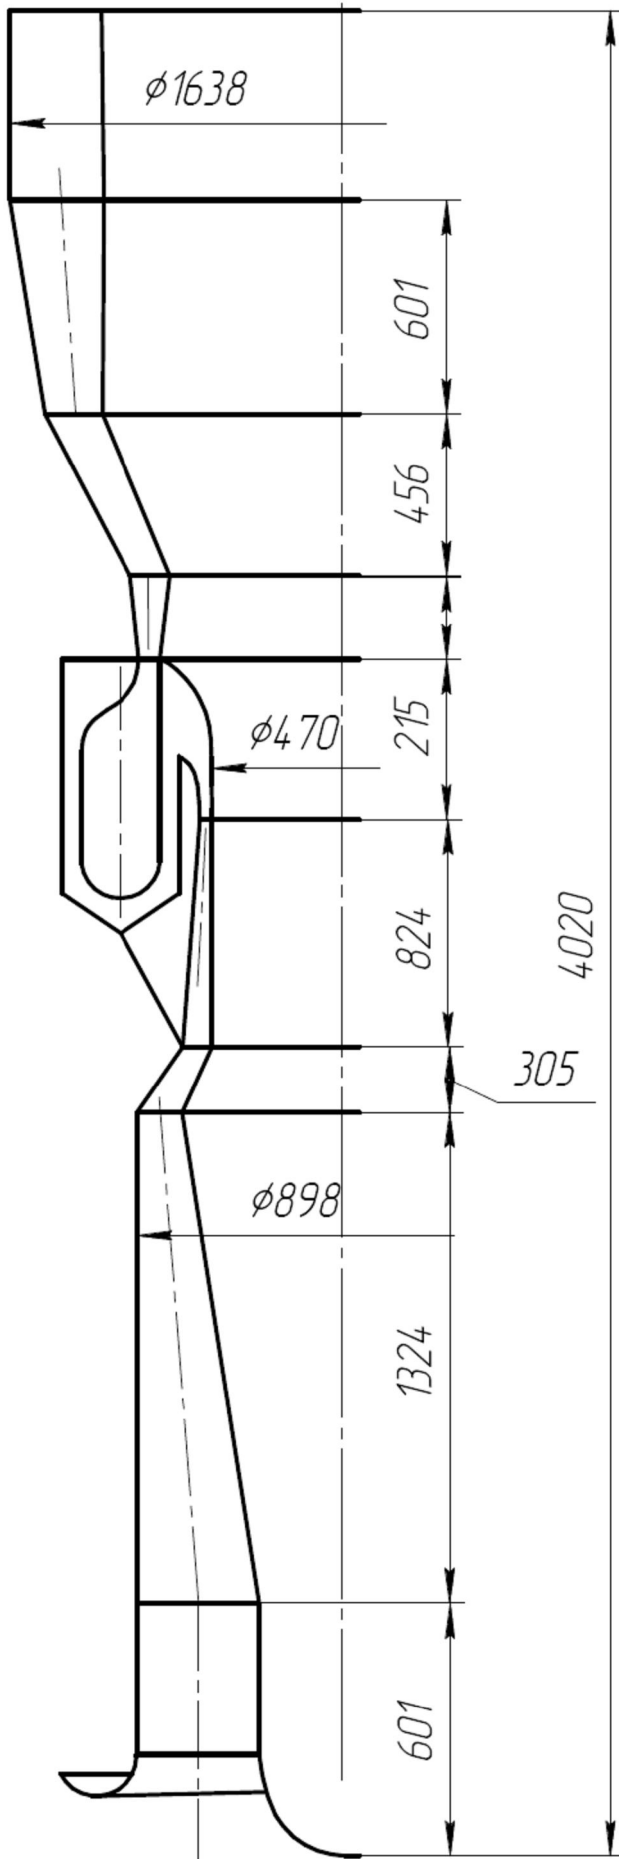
Ескіз поздовжнього перерізу ГТД
